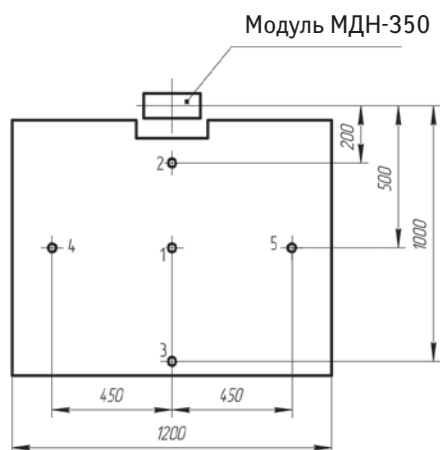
Расположение точек нагрузки при испытаниях на стенде
